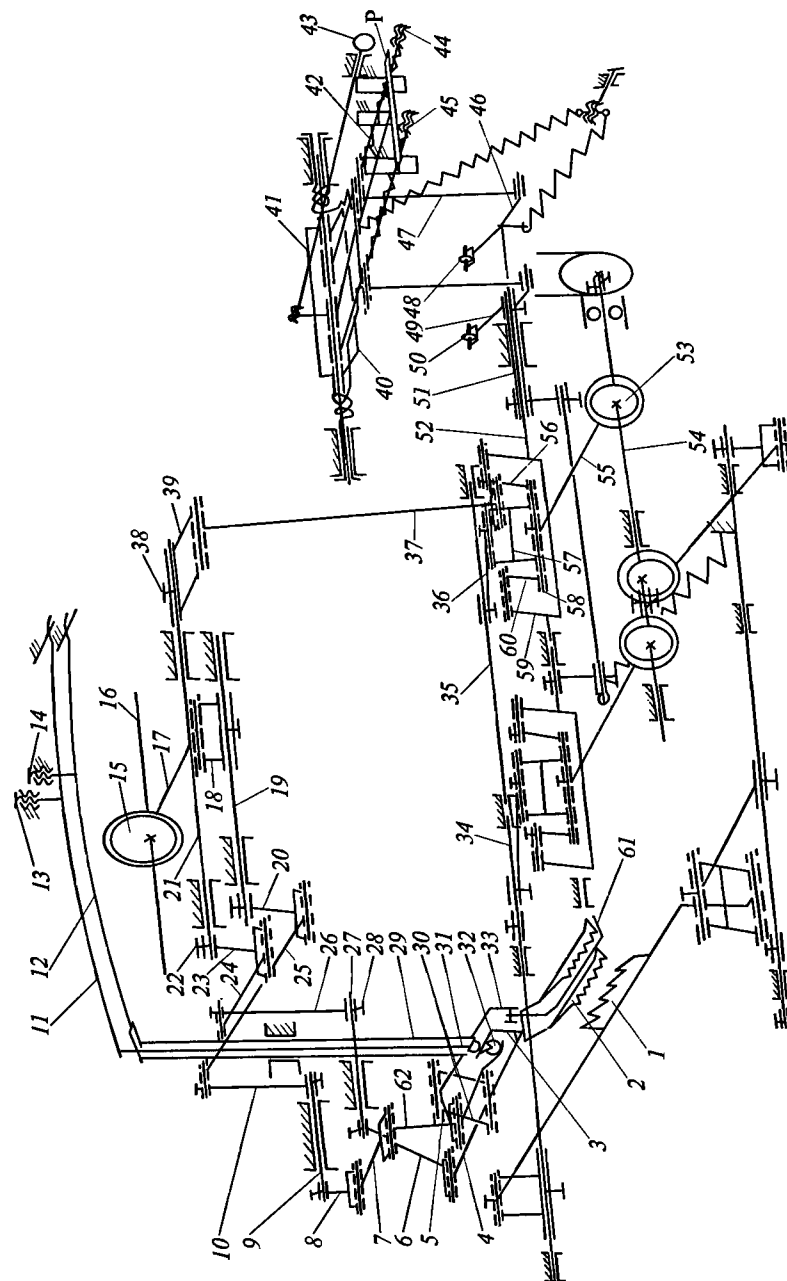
Кинематическая схема механизма двигателя ткани с верхней и нижней транспортирующими рейками
